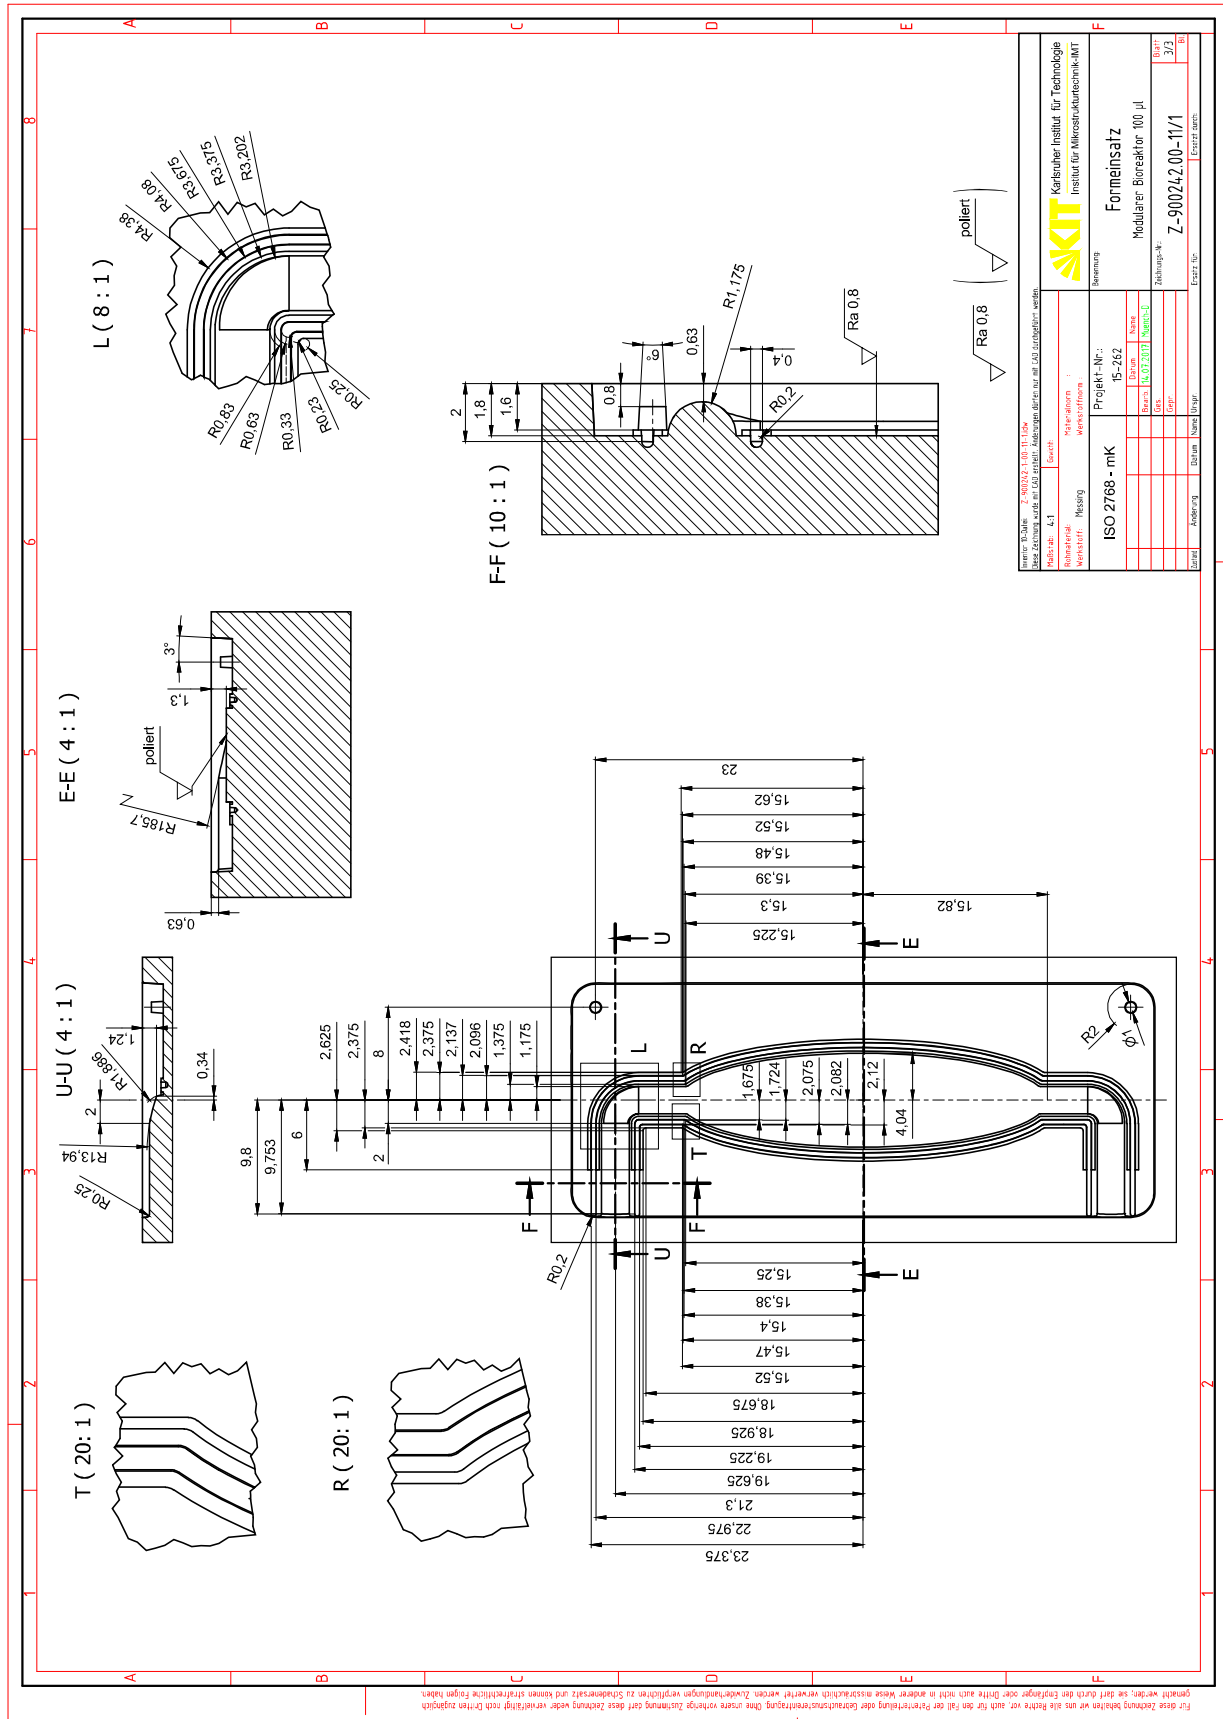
Technische Zeichnung der Versorgungskammer des Formeinsatzes zur Abformung der Chiphälften für den 100 µl-MBR.
